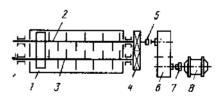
Схема двухвального смесителя: 7 - корпус; 2 - ведущий вал; 3 - ведомый вал; 4 - шестерни; 5 - уравнительная муфта; 6 - редуктор; 7 - муфта; 8 - электродвигатель
